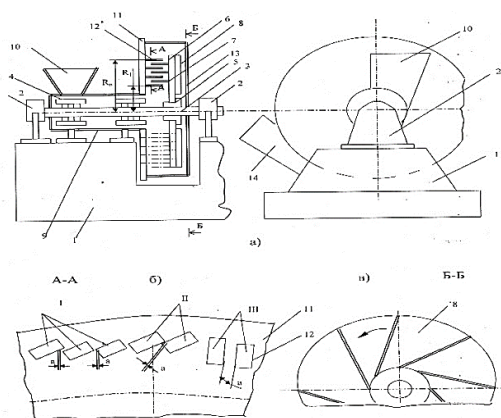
Схема дисмембратора (общий вид (а); диск с пальцами – сегментами (б); диск вентиляционный с лопастями (в): 1-станина; 2-кронштейн; 3-вал; 4-била; 5-втулка; 6, 7-диск с пальцами; 8-диск вентиляционный; 9-полая труба; 10- бункер; 11-диск с пальцами; 12- пальцы; 13-кожух; 14-патрубок
